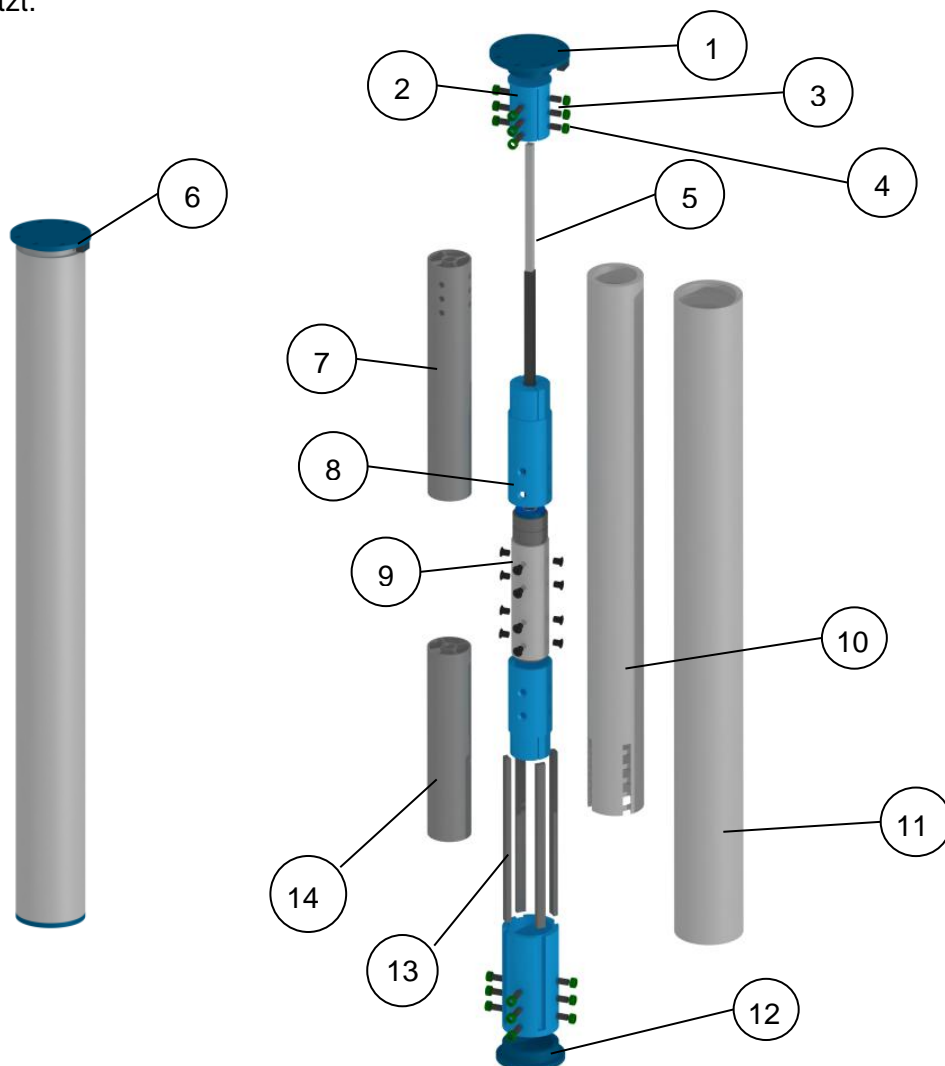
Rollengewindetrieb eingefahren (links), Explosionsbild (rechts)
